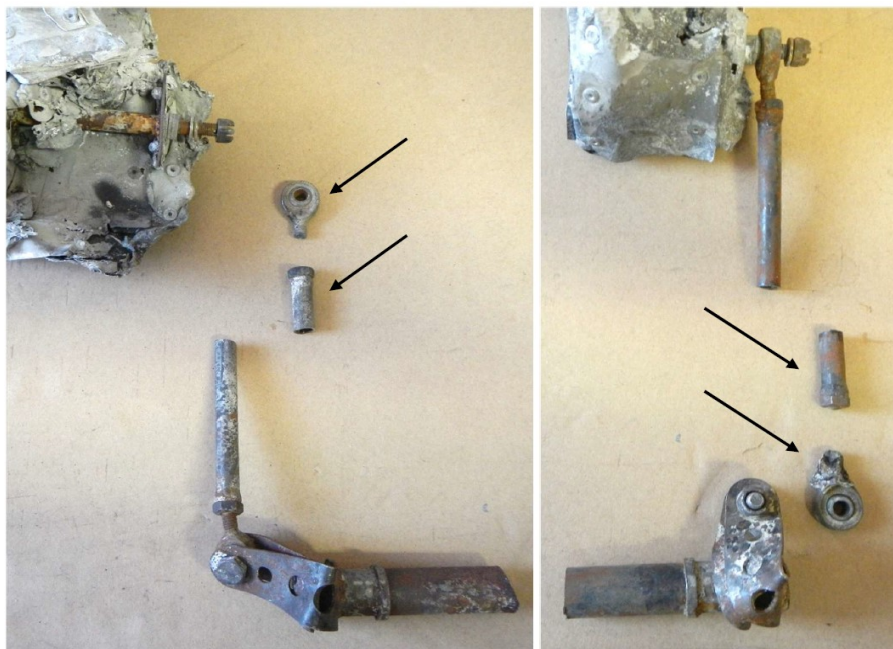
Detail zajišťovacích pojistek na hřídeli reduktoru
